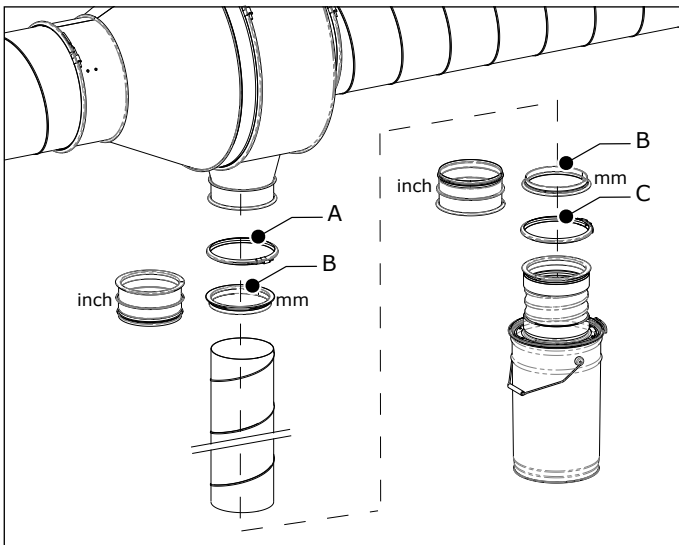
Montage du bac à poussière par un conduit vertical
